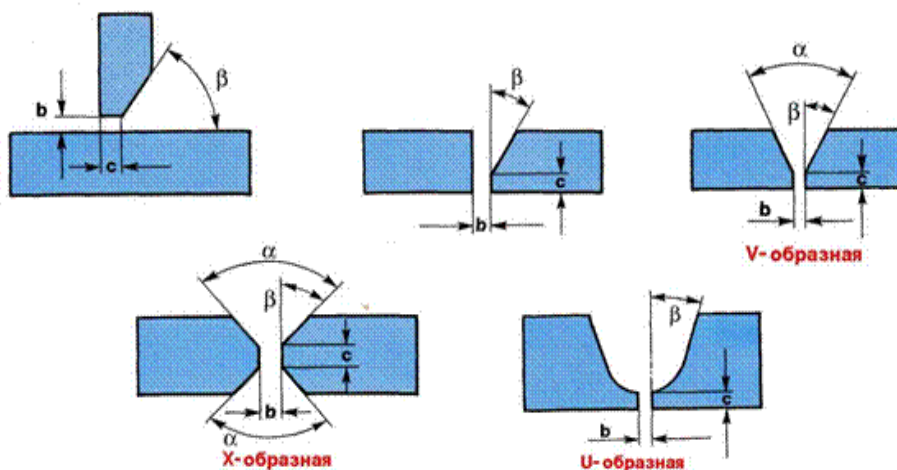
Конструктивные элементы сварных соединений
